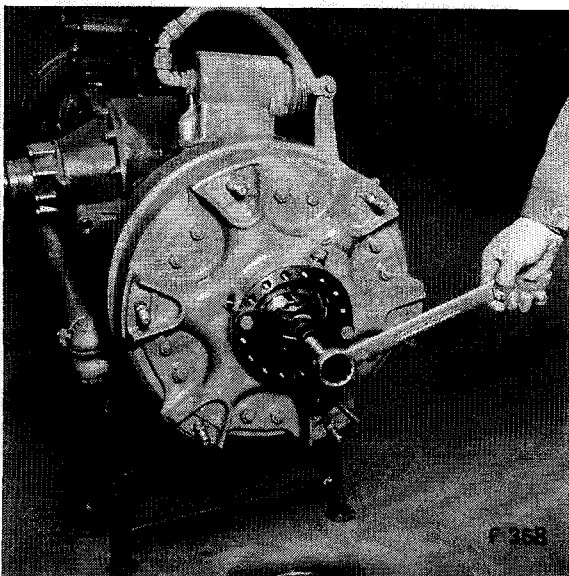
Lösen der Befestigungsschrauben der beiden Segmentsicherungen
